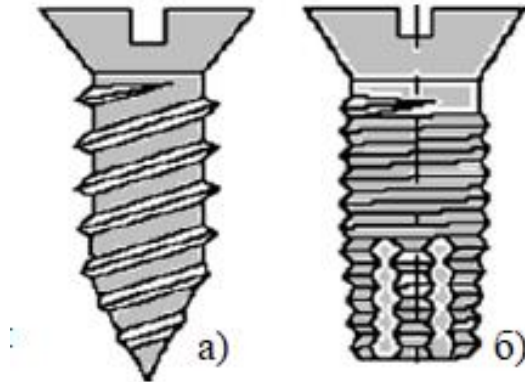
Самонарізні гвинти: а – формувальний; б – різальний
